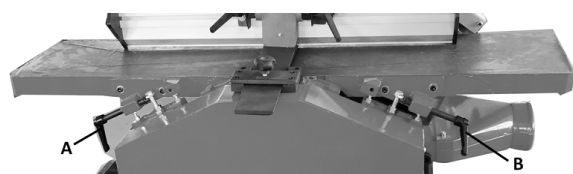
Umrüsten von Abrichthobel auf Dickenhobel
